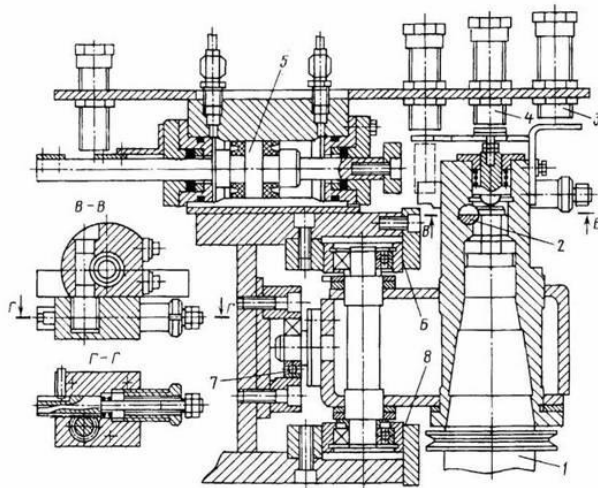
Инструментальный магазин в позиции смены инструмента
